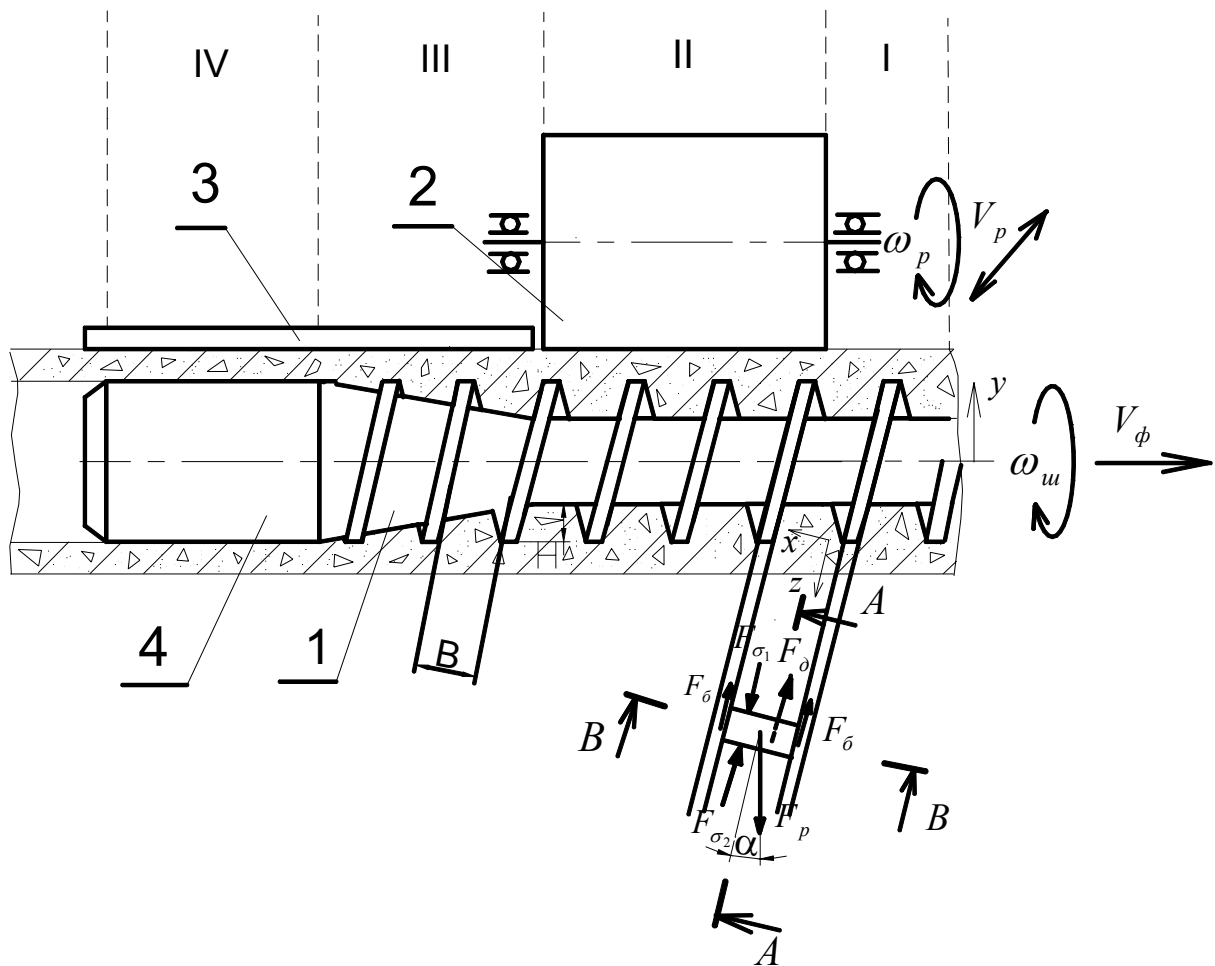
Розрахункова схема процесу ролико-екструзійного формування
